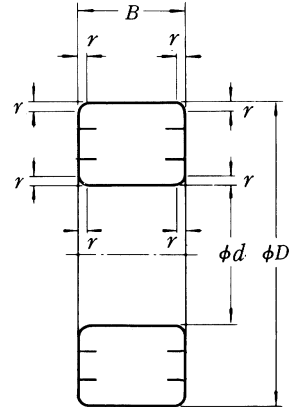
Габаритные размеры радиальных шарикоподшипников и роликоподшипников
